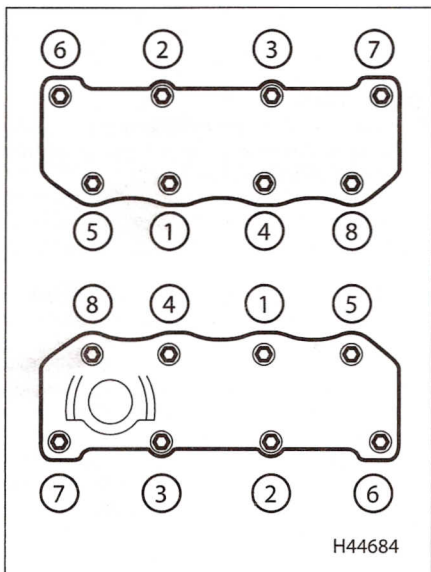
Последовательность затяжки болтов крепления крышки головки цилиндров
